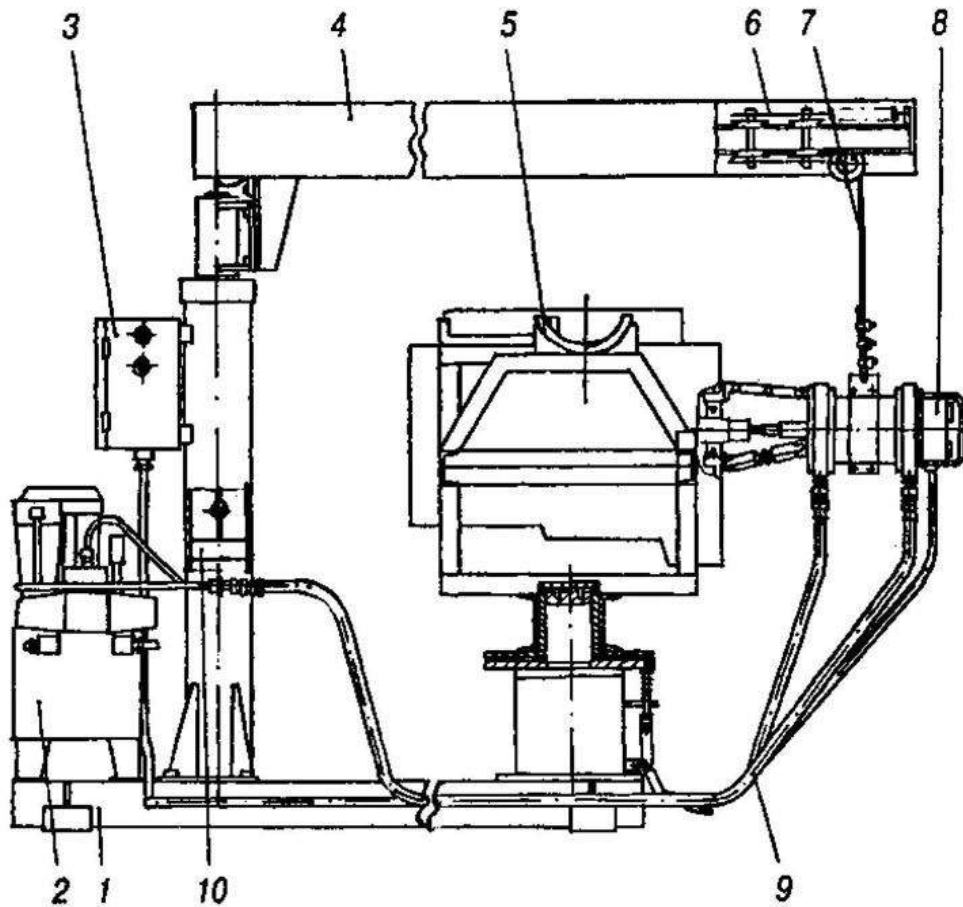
Схема станда для розбирання-складання вузлів і агрегатів шасі тракторів класу 3: 1 — станина; 2 — гідростанція; 3 — електрошафа; 4 — стріла; 5 — ложемент для кріплення агрегату; 6 — каретка; 7 — канат; 8 — гідроциліндр; 9 — рукав високого тиску; 10 — противага
